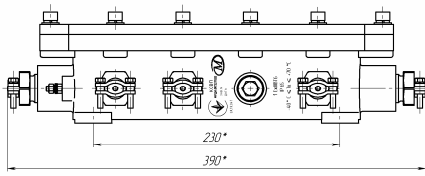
Внешний вид и габаритные размеры коробки соединительной КСВ
